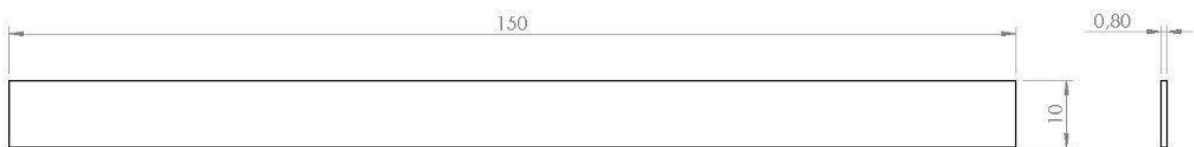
Dimensão do provete em APET para ensaio de tração.
